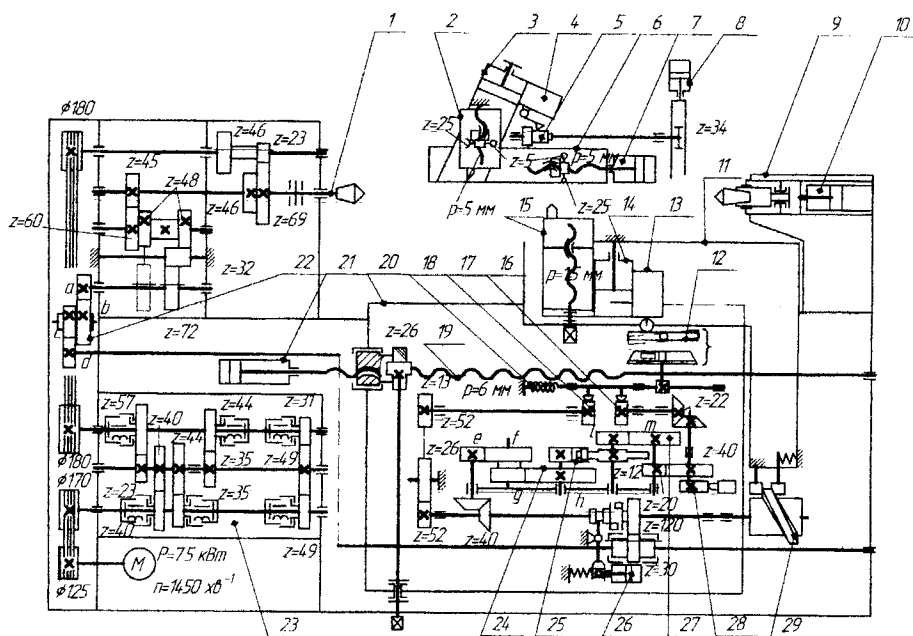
Кінематична схема різьботокарного напівавтомата 1Б922
